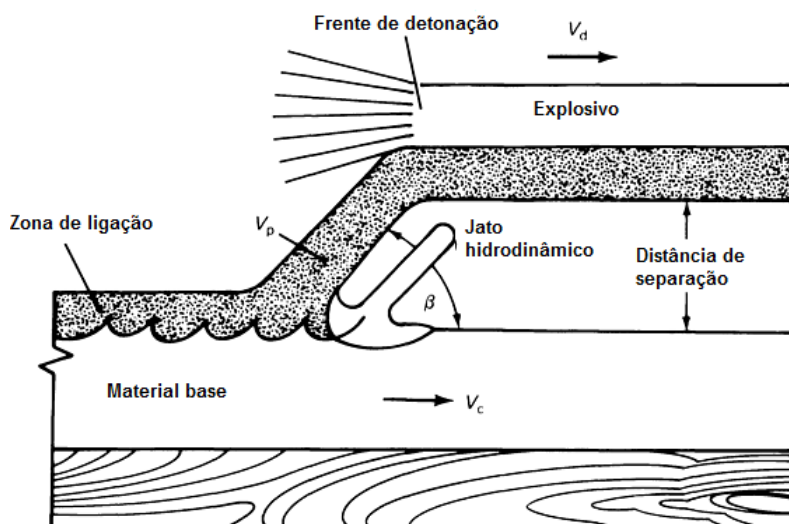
Desenho esquemático do processo de soldagem explosiva. Adaptado de [26].
